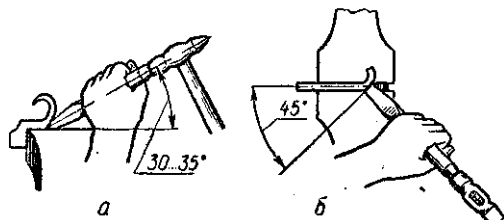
Рубання листового металу в лещатах: а, б — нахил зубила відповідно до оброблюваної поверхні та осі губок
